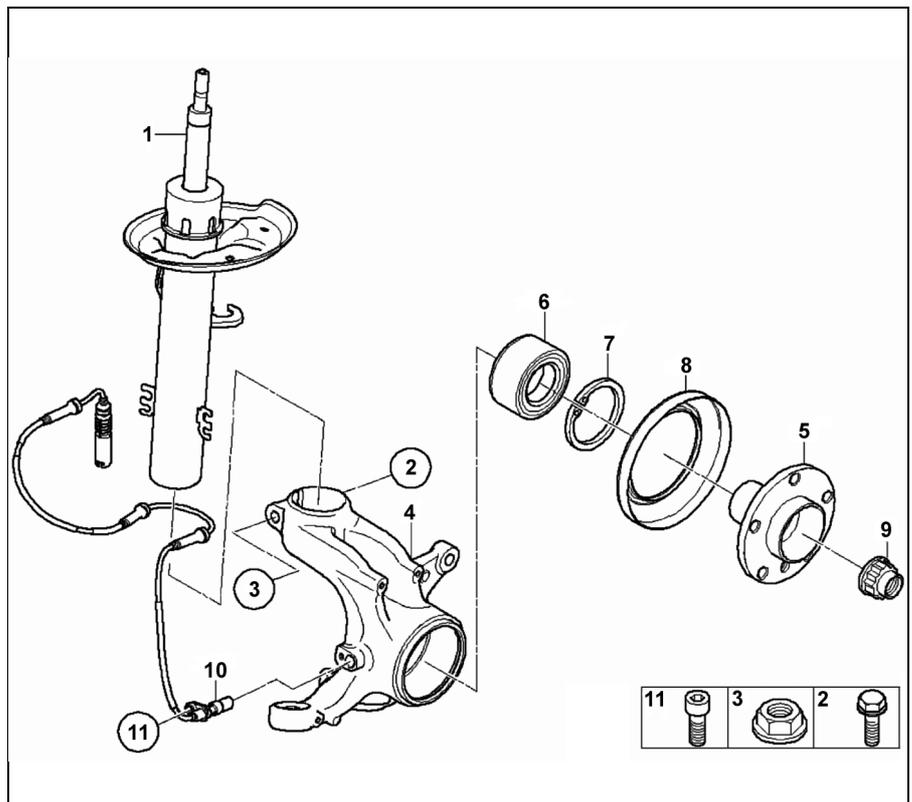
Амортизационная стойка. 1 - амортизационная стойка, 2 - болт (M12x1,5x80), 3 - гайка (M12x1,5), 4 - поворотная опора, 5 - ступица выходного фланца дифференциала, 6 - шарикоподшипник, 7 - стопорное кольцо, 8 - пылезащитная манжета, 9 - гайка с буртиком (M27x1,5), 10 - датчик системы "DSC" (L=832 мм), 11 - болт (M6x16).
